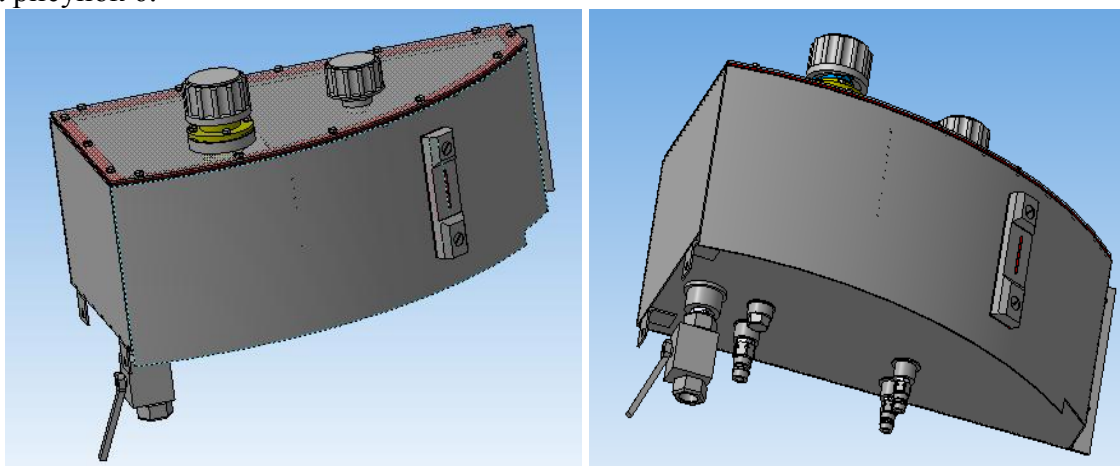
Сборочная 3D-модель гидравлического бака
